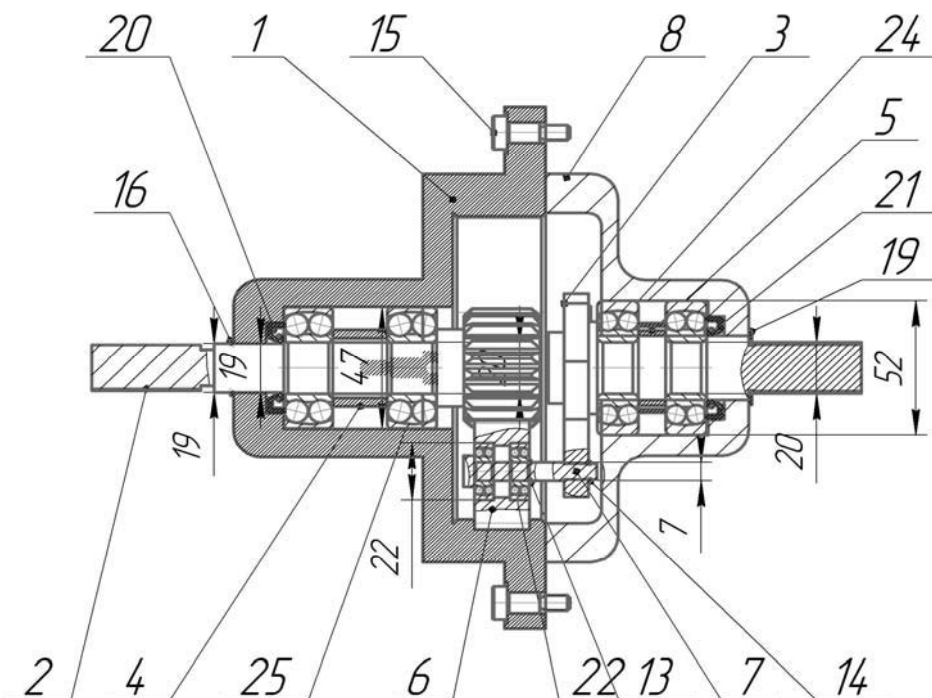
Чертеж проекционного вида редуктора с позициями
